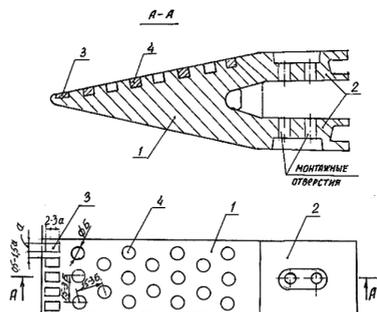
Зуб ковша экскаватора, армированный вставками из износостойкого чугуна: 1 – корпус; 2 – хвостовик; 3 – вставка параллелепипедной формы; 4 – вставка цилиндрической формы
